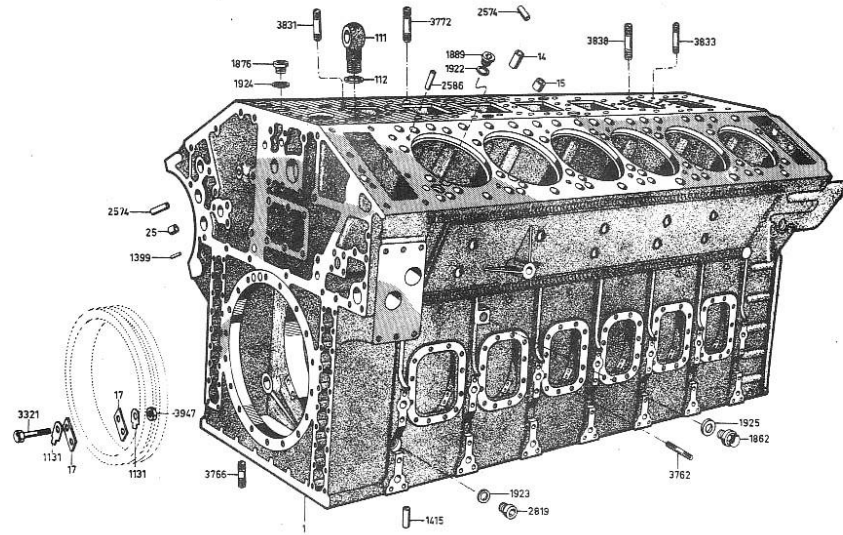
DIESEL ENGINE. (16 V 538.)
